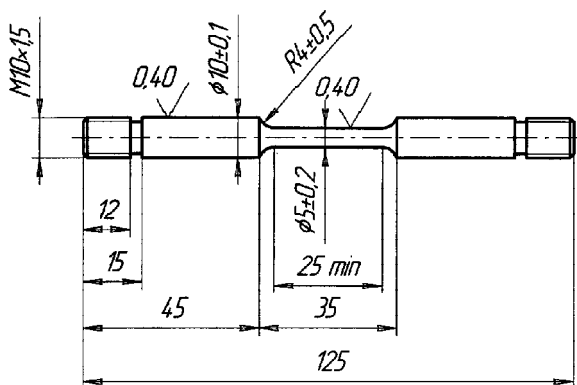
Чертеж образца для испытаний монокристаллического жаропрочного сплава ЖС26-ВИ на релаксацию
